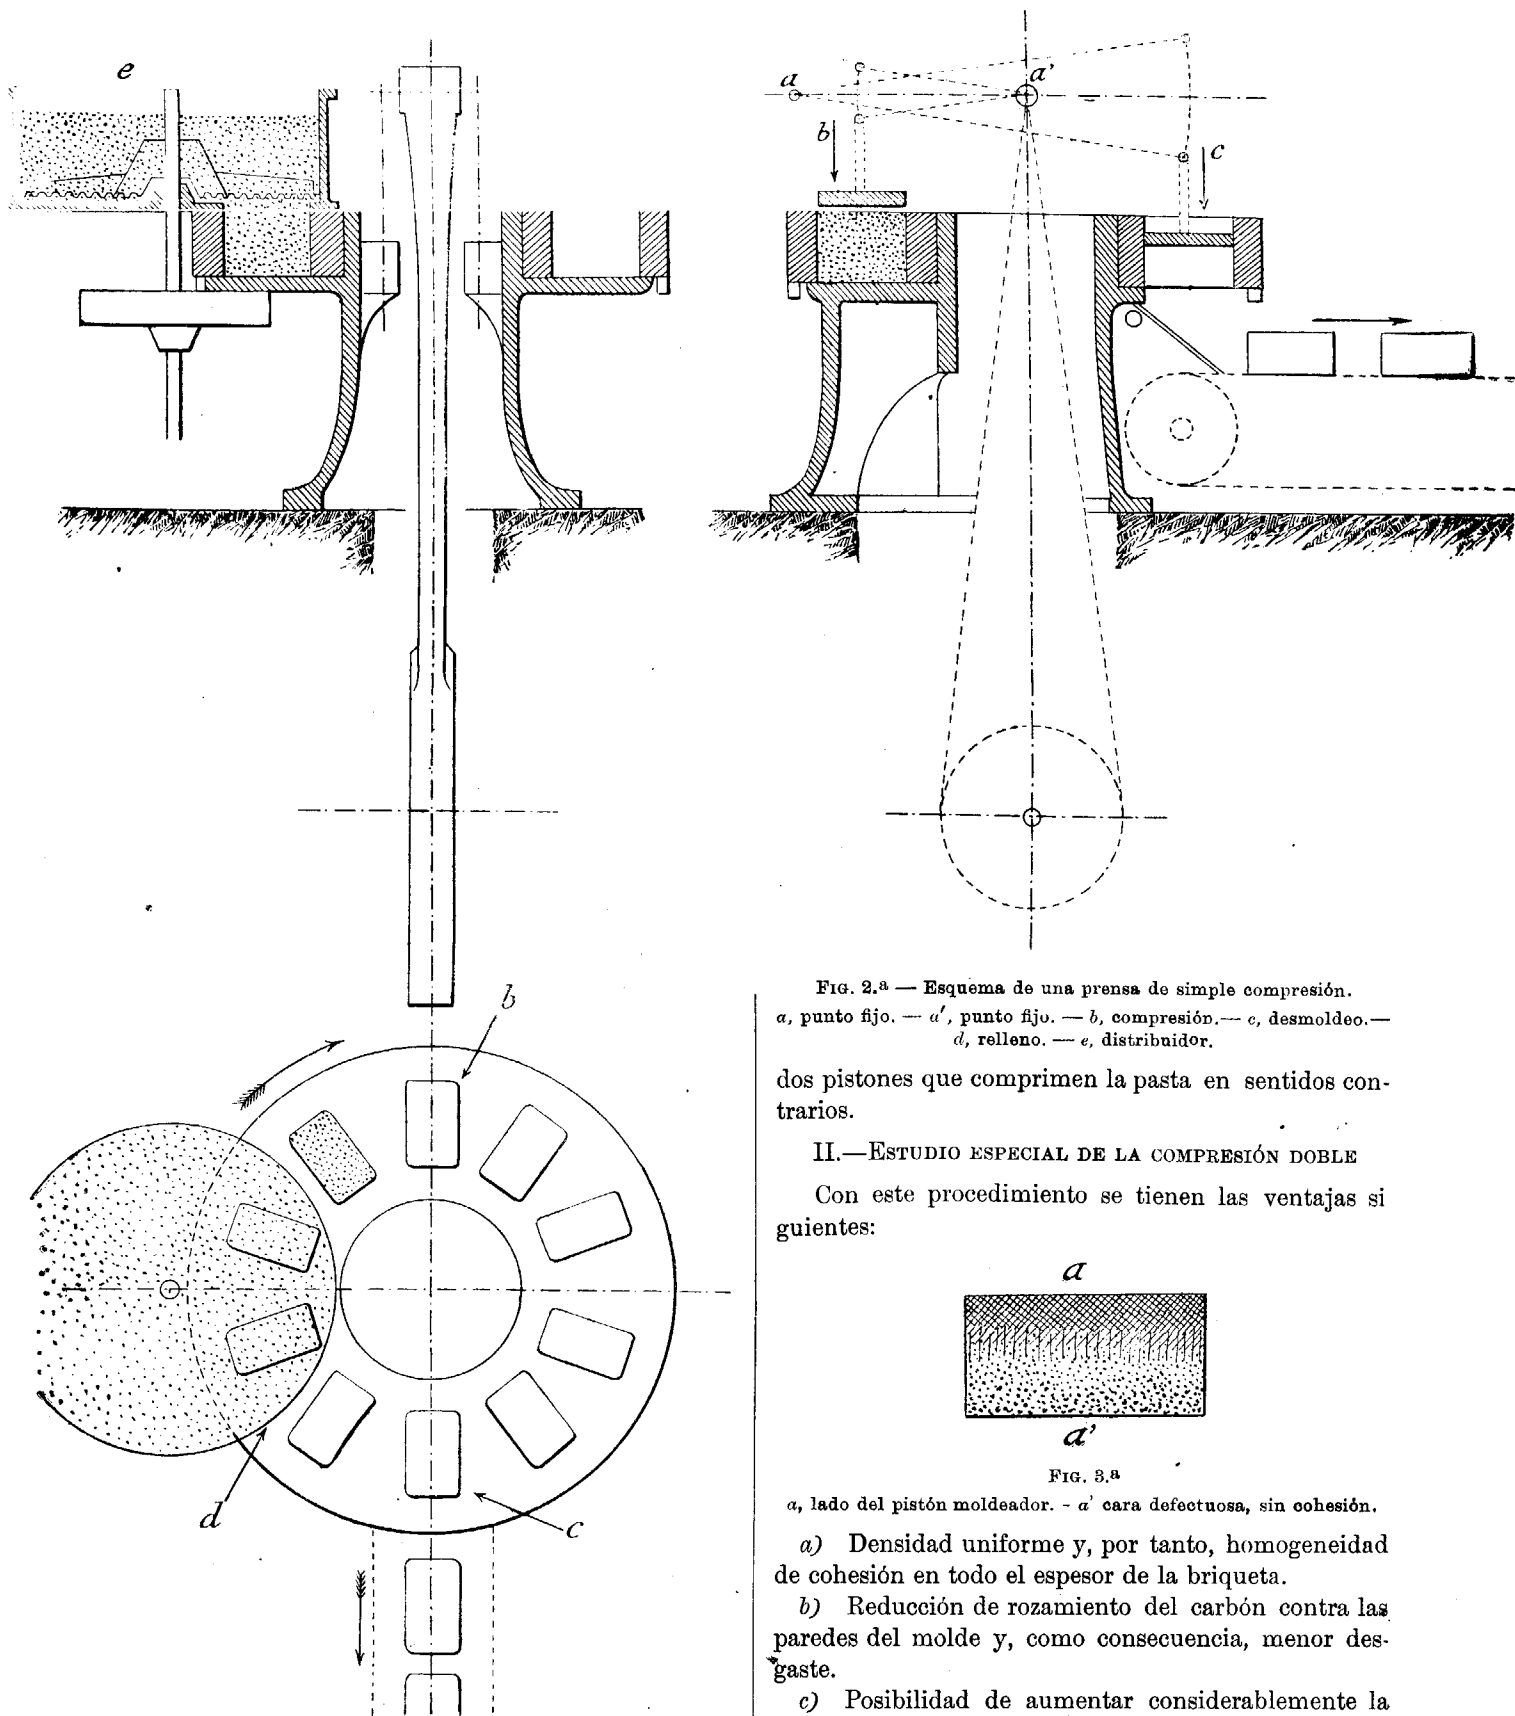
^a — Esquema de una prensa de simple compresión. a, punto fijo. — a', punto fijo. — b, compresión. — c, desmoldeo. — d, relleno. — e, distribuidor.
